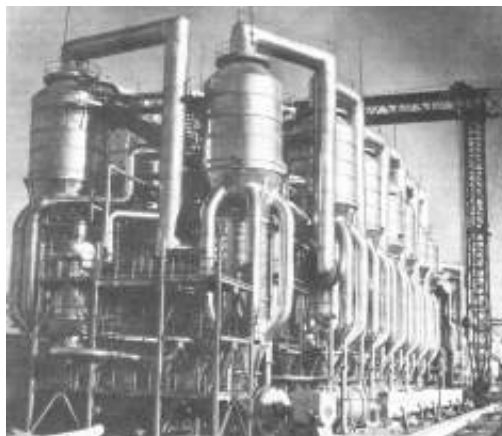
Сварные конструкции Шевченковского атомного реактора на быстрых нейтронах
